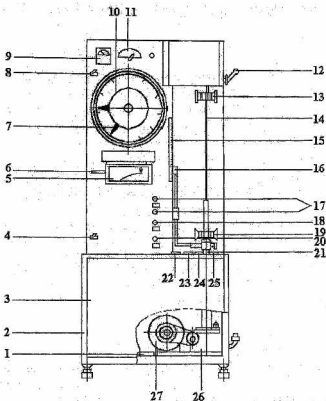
Общий вид машины разрывной РМУ-0,05-1:
